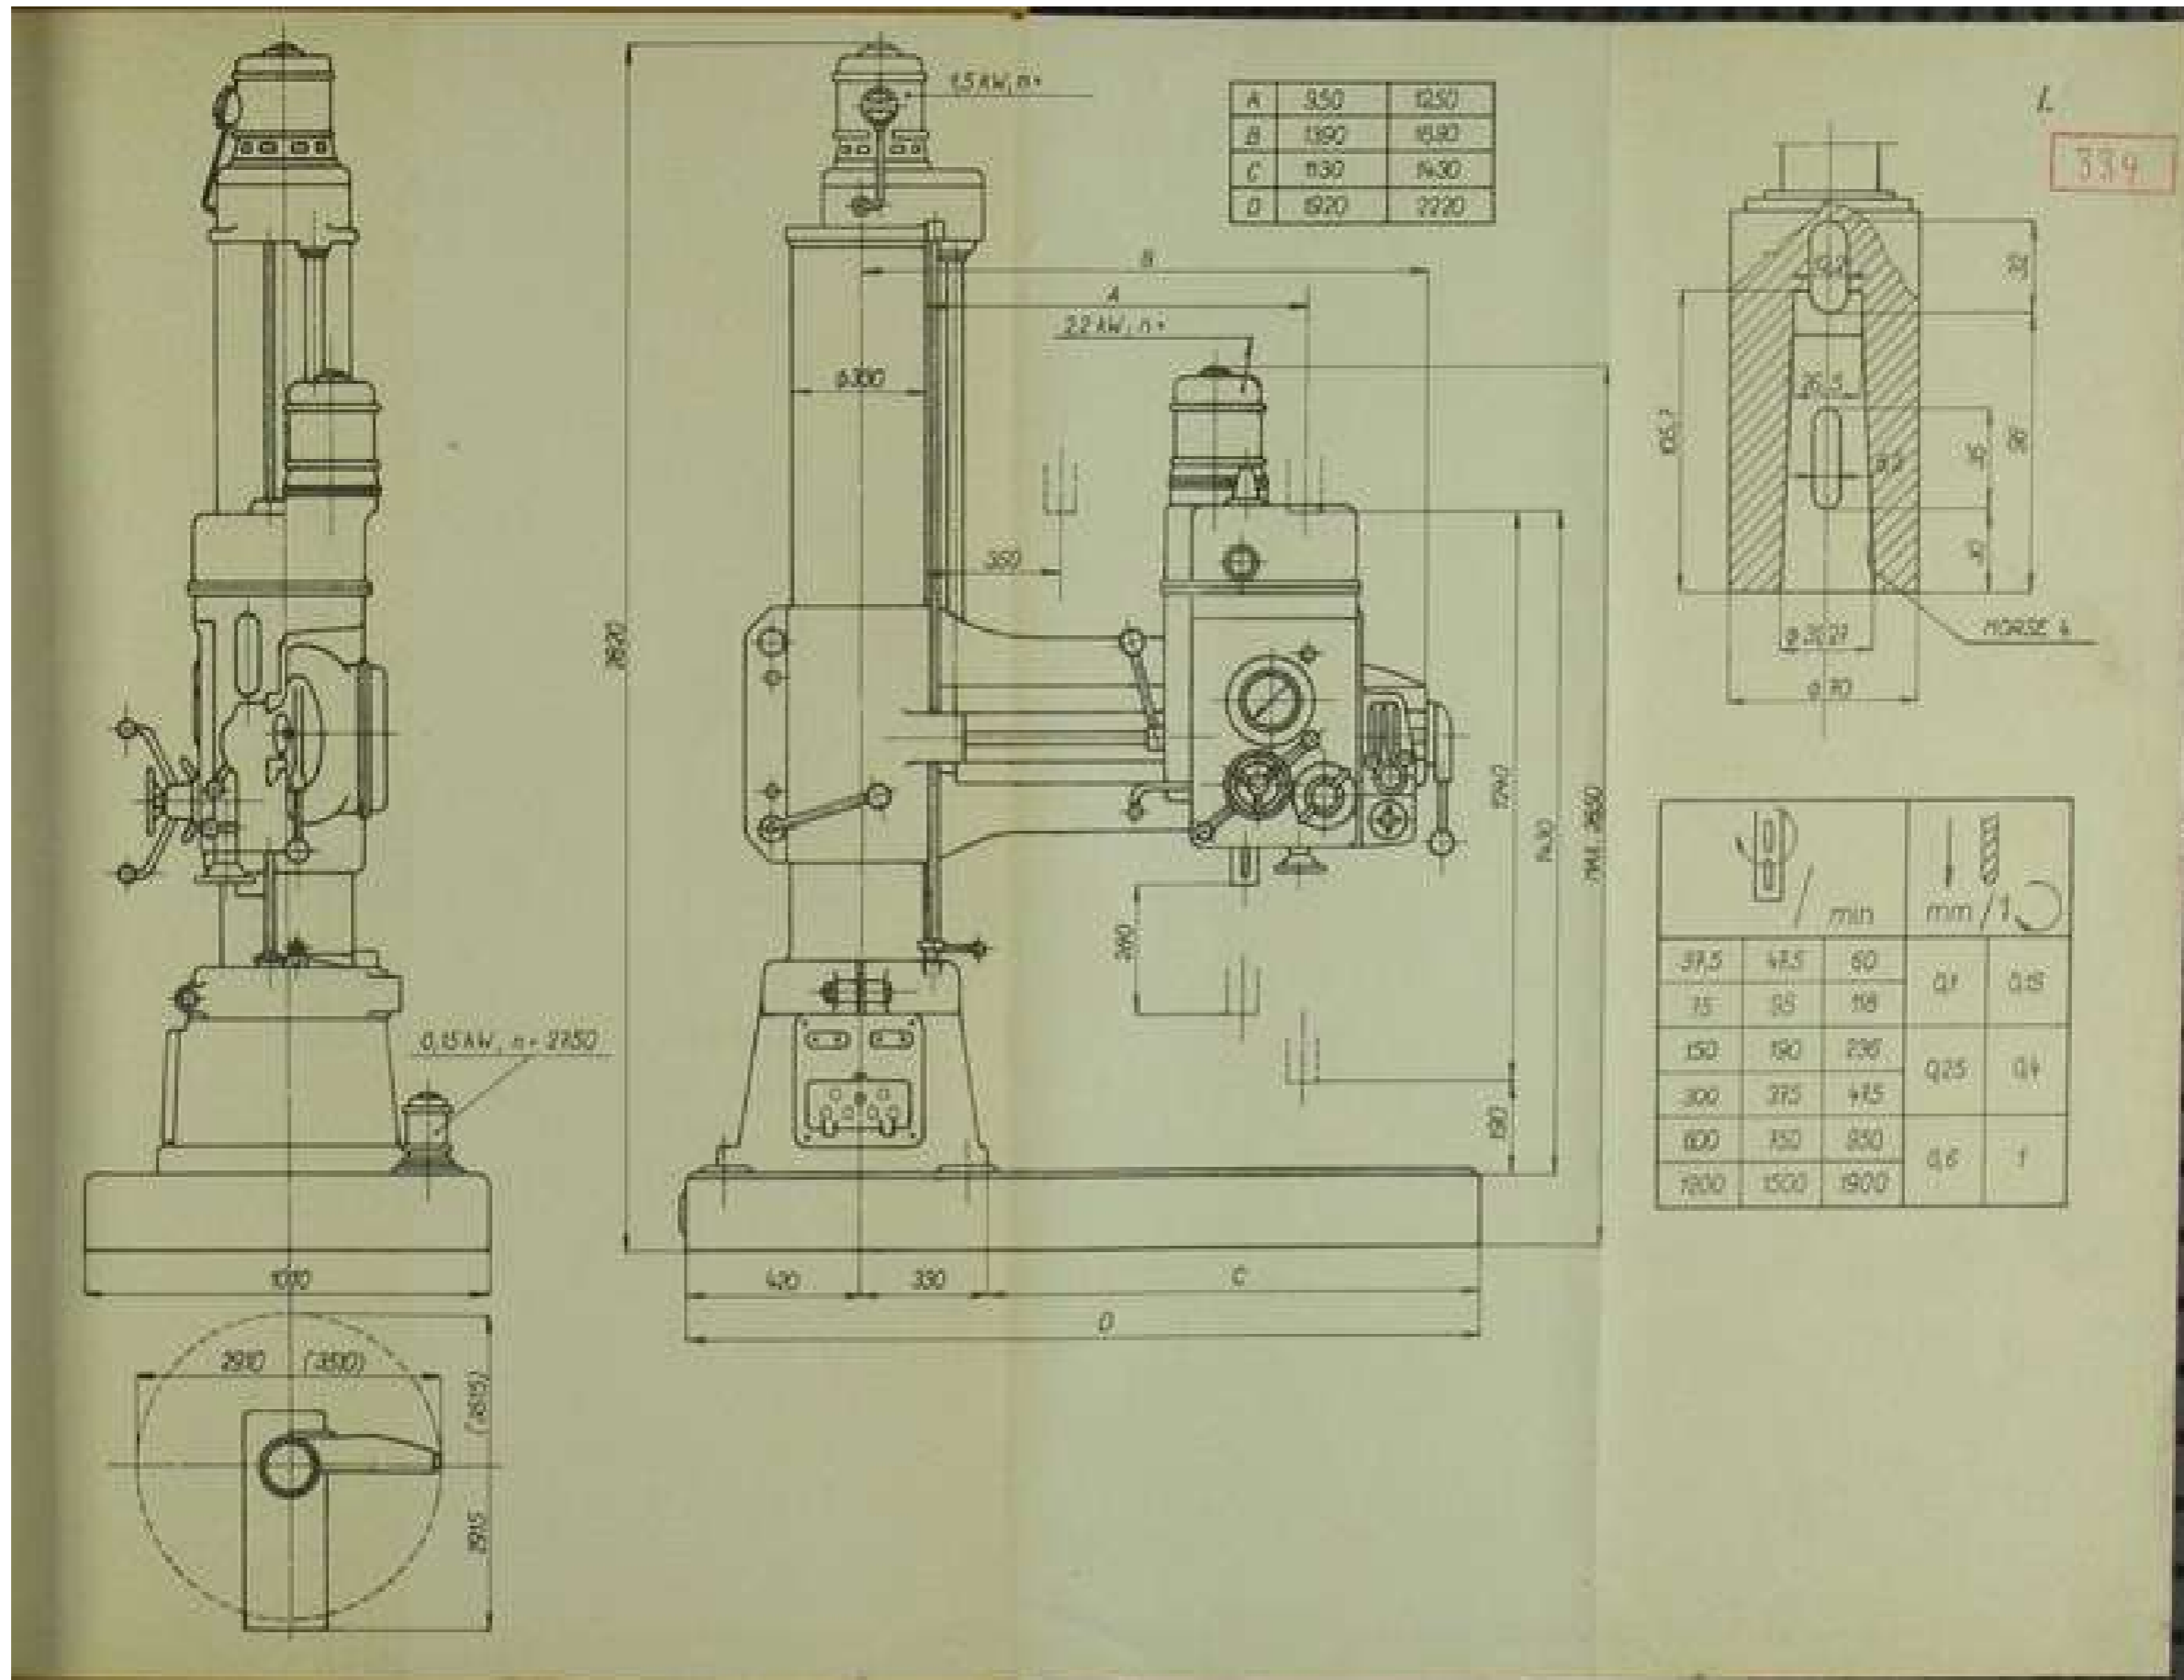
Dessin technique de la perceuse radiale (Radial Bohrmaschine) installée à la carrière, Bedienungsanweisung für die Radial-Bohrmaschine MAS Type RV 40 (TTS Arolsen).
